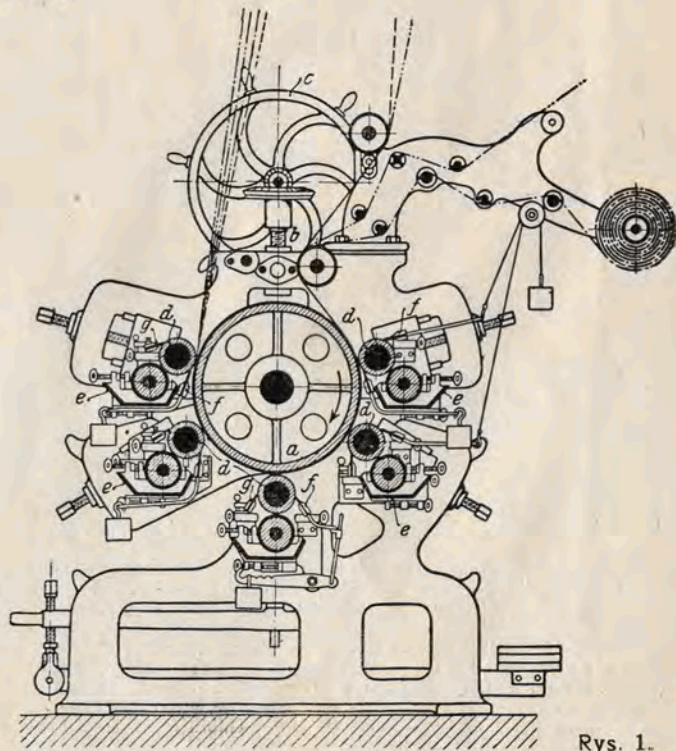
przedstawia nam przekrój pięciowalcowej drukarki firmy Ssów F. Zimmera.
